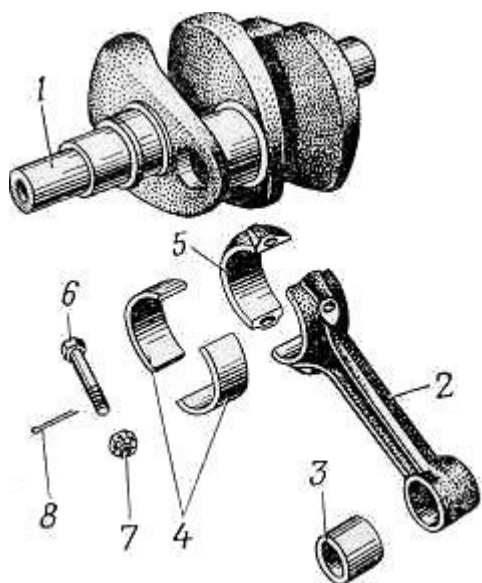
Детали кривошипно-шатунного механизма двигателя МТ-801:
